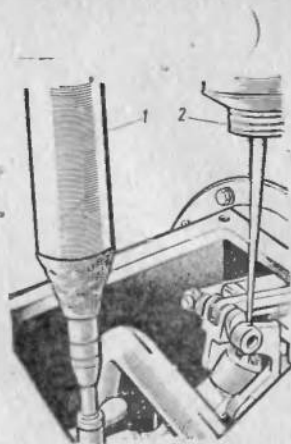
Шприцевание подшипника каретки и смазывание нажимных устройств:
